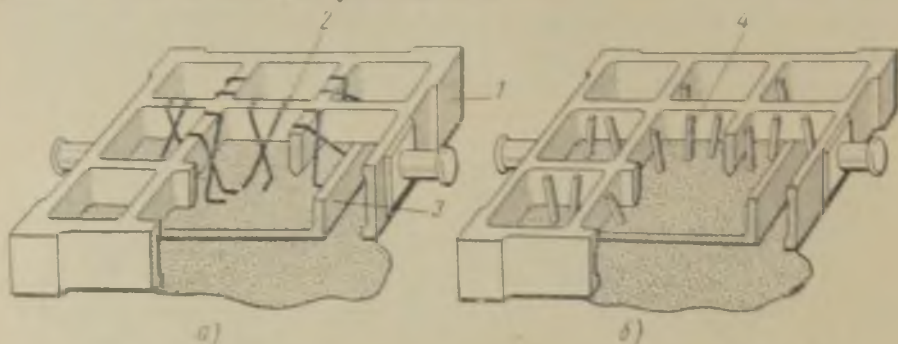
Установка в верхней опоке солдатиков и крючков при изготовлении формы
